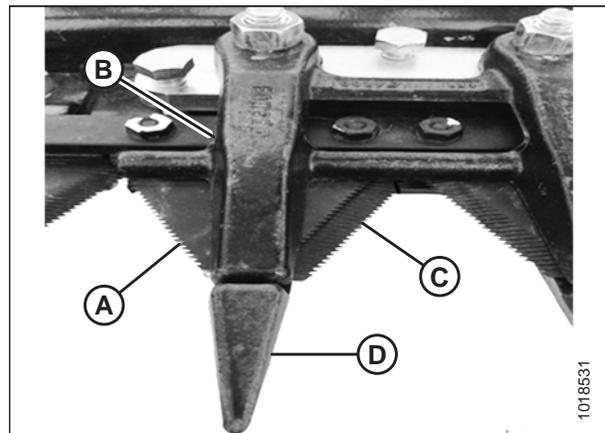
Mécanisme de retenue du doigt central sur couteau double
